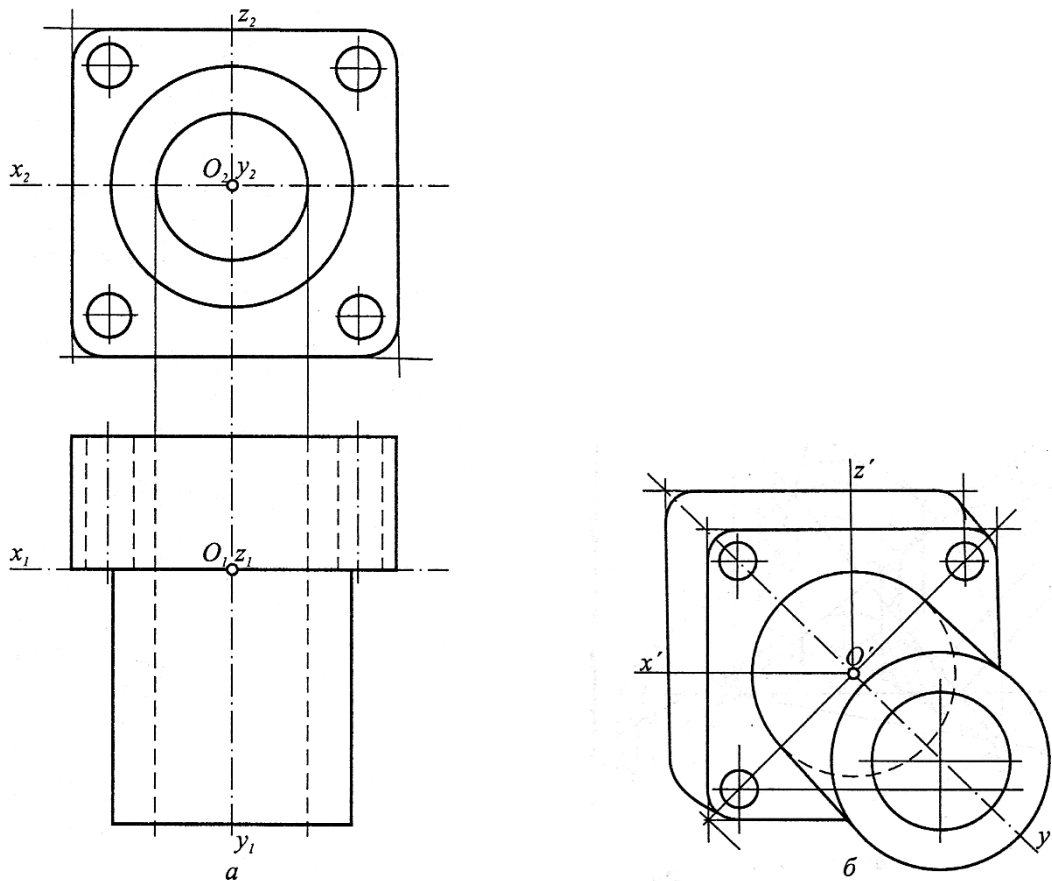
a* – вид спереду, вид зверху деталі; *б* – аксонометрія деталі у ФД
